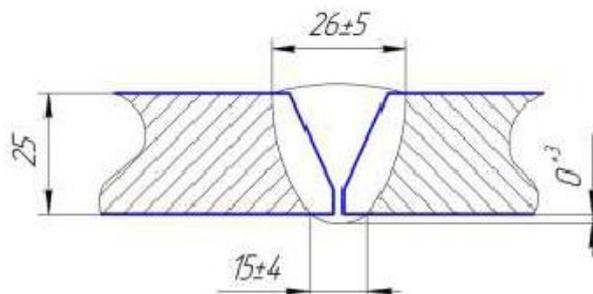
Конструктивные размеры сварного шва
